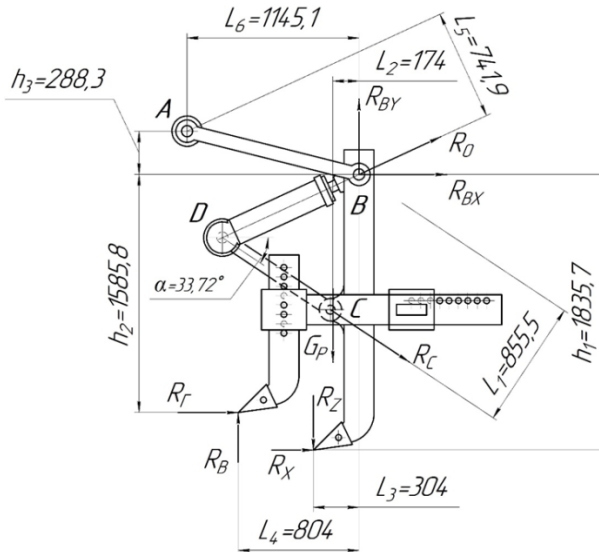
Расчетная схема для определения усилия на штоке гидроцилиндра
